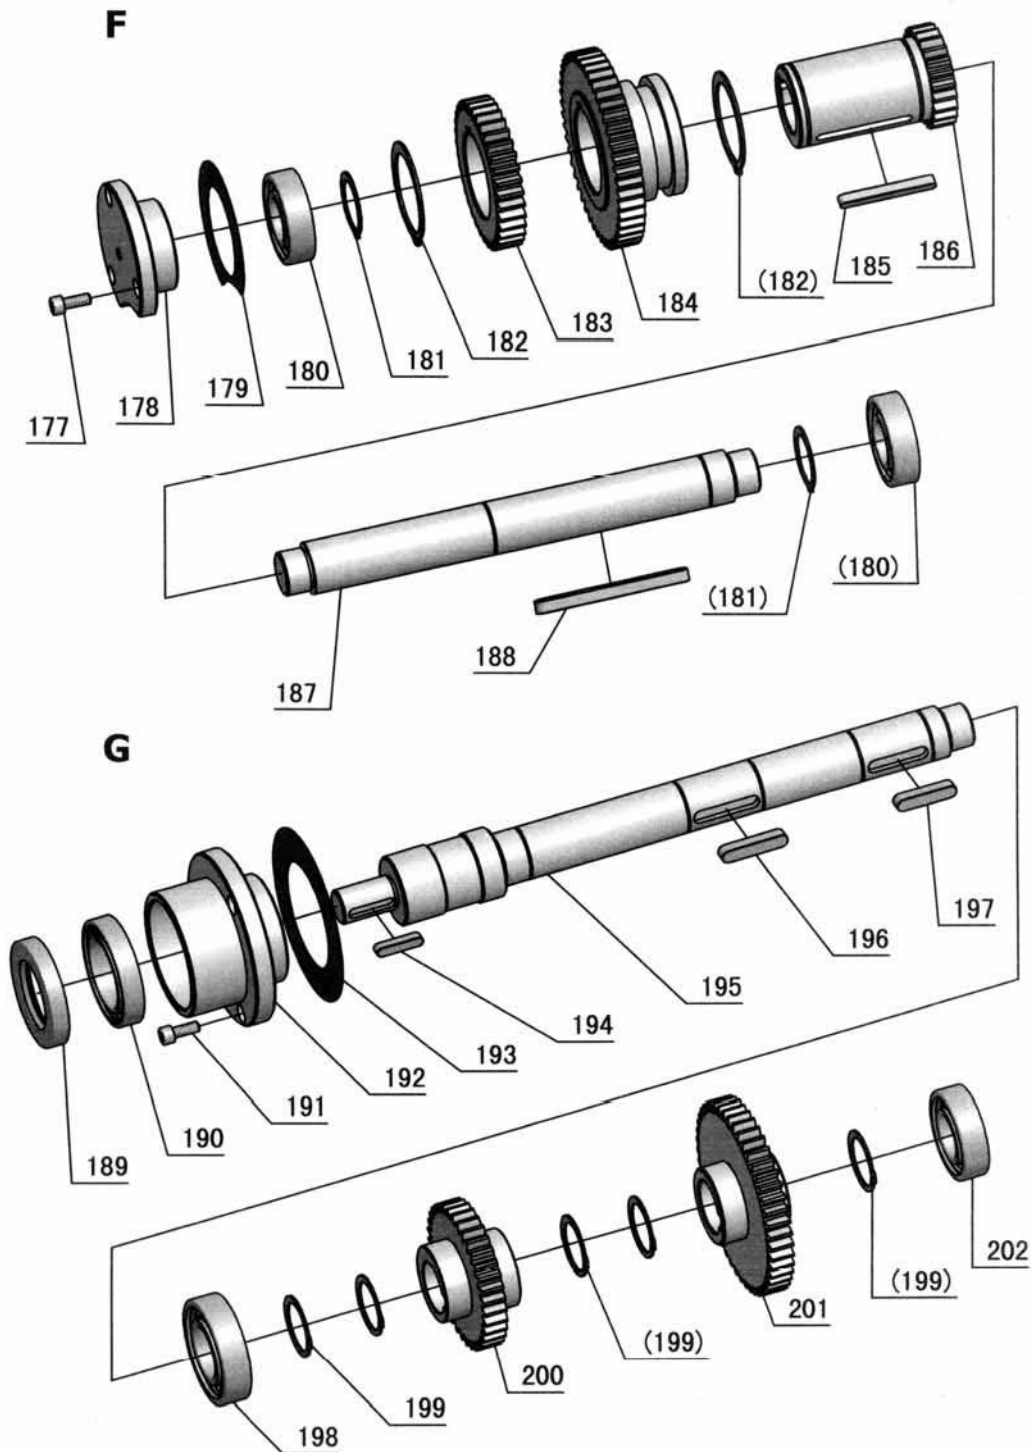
Spindelstock 7 von 8 - Headstock 7 of 8
